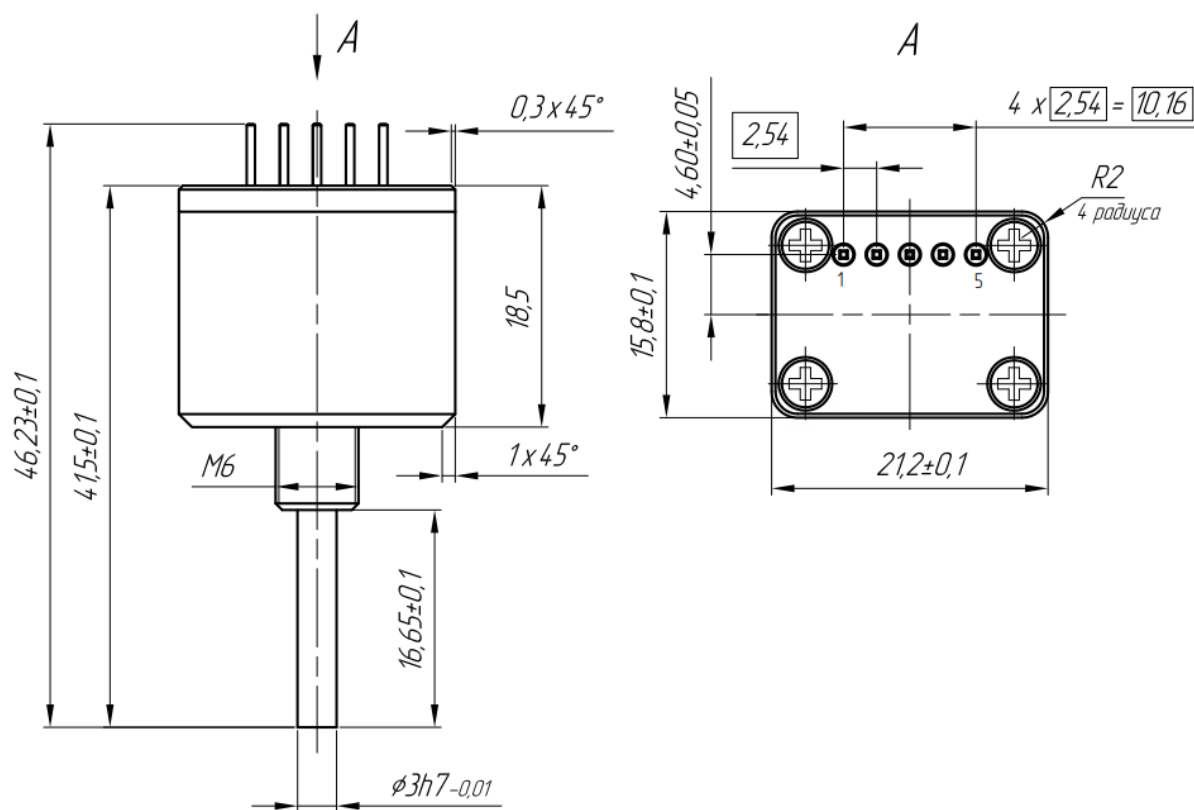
Установочные и присоединительные размеры энкодера
